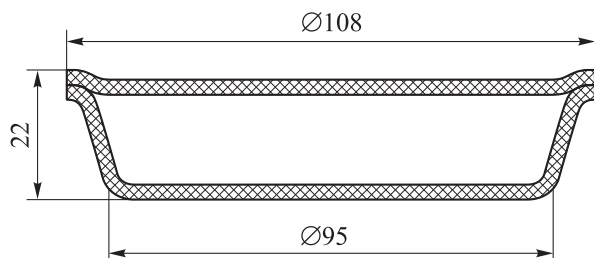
Схема полиэтиленовой банки для упаковки жидких продуктов
